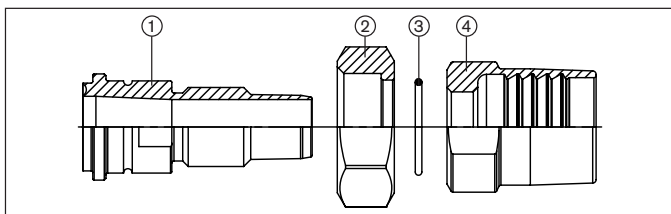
Montage der Anschlüsse Steril Standard mit Schlauchmutter
